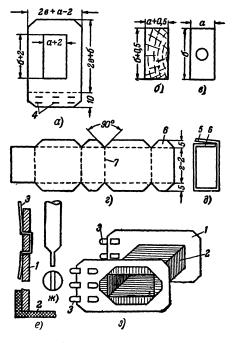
Изготовление каркаса. a — разметка щечек; δ — шаблон-брусок для склейки каркаса; δ — брусок для намотки; ϵ — разметка заготовки гильзы каркаса; δ — склейка концов гильзы; ϵ — крепление в щечке каркаса самодельных контактных лепестков; ∞ — пробойник; δ — общий вид готового каркаса.
